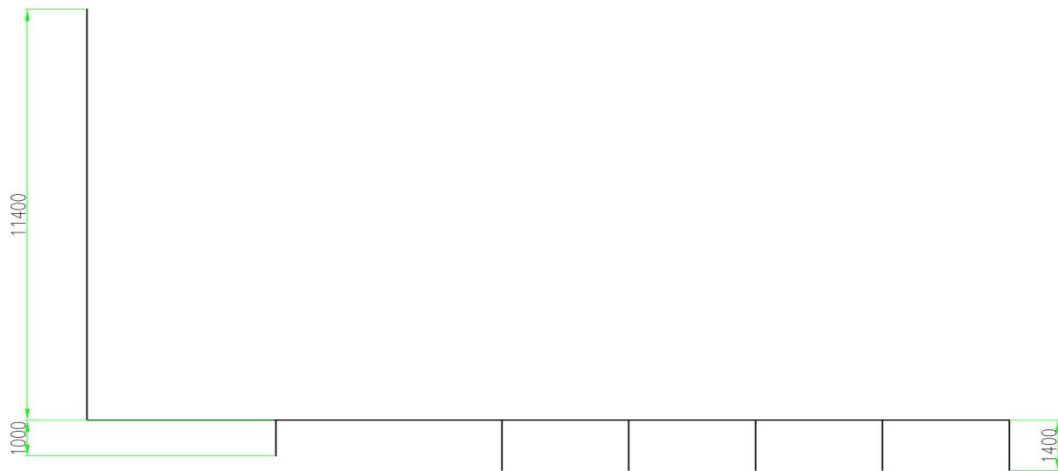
(Vista longitudinal de la tubería de lastre)
